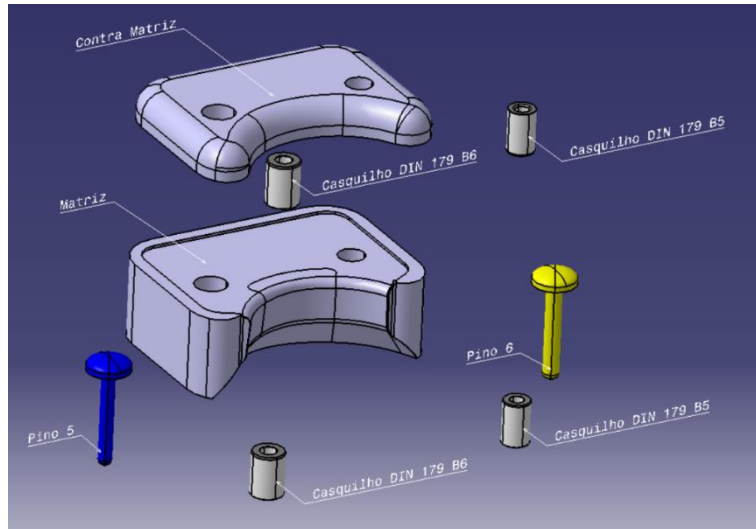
Vista explodida do conjunto final montado do produto (Ferramenta) em modelação 3D.
